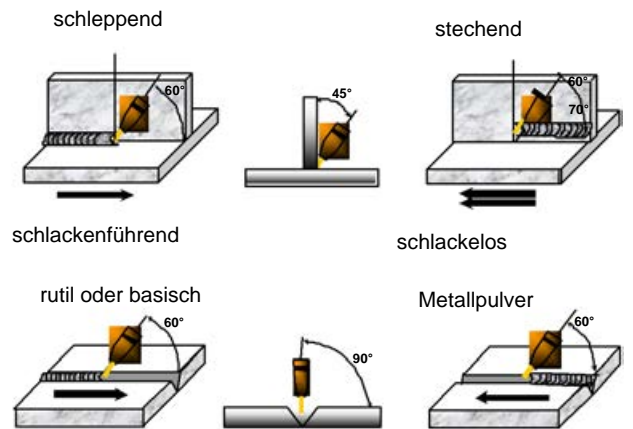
Brennerwinkel und Brennerführung beim Schweißen mit Fülldrähten
